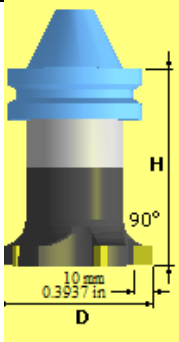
Бібліотека вибору різальних інструментів для фрезерного верстата з ЧПК
